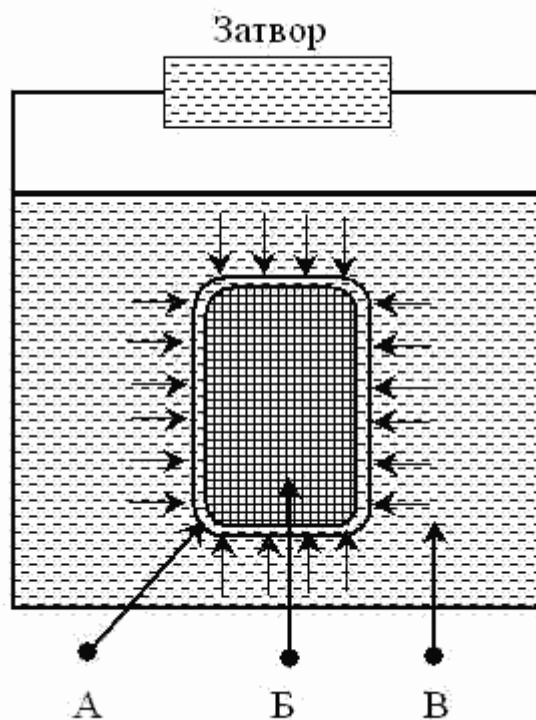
Схема изостатического прессования А – оболочка Б – заготовка В - рабочая жидкость
